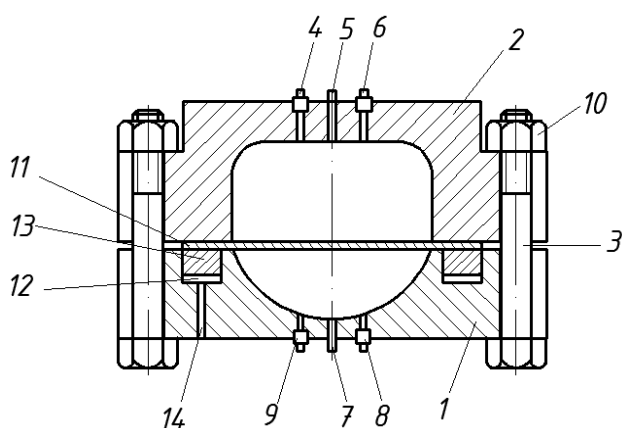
Схема устройства для штамповки с кольцевым поршнем:
